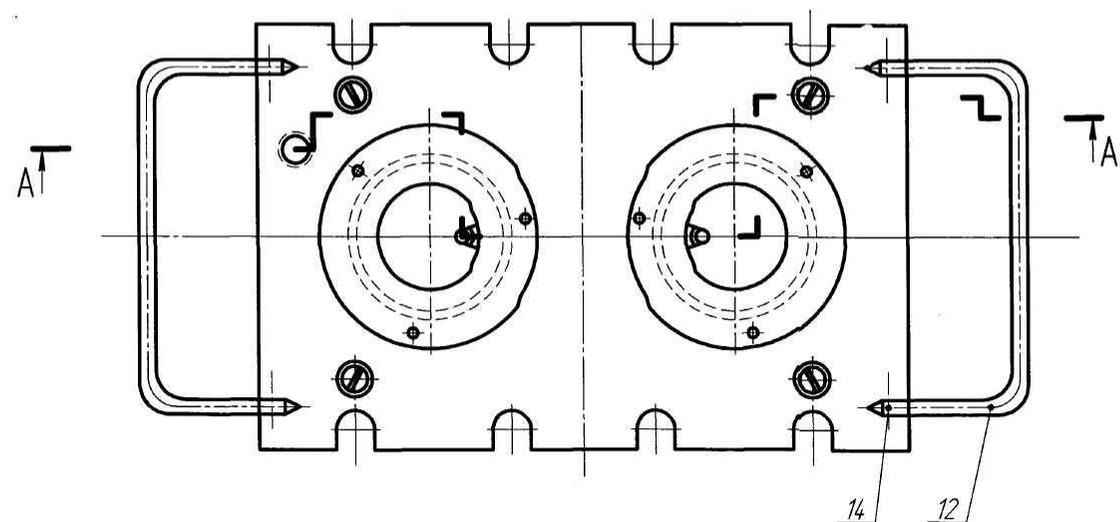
Пресс-форма съемная для изготовления деталей методом литьевого прессования:
